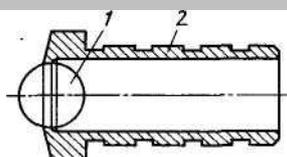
Пневматический контактный преобразователь с шариковой заслонкой
